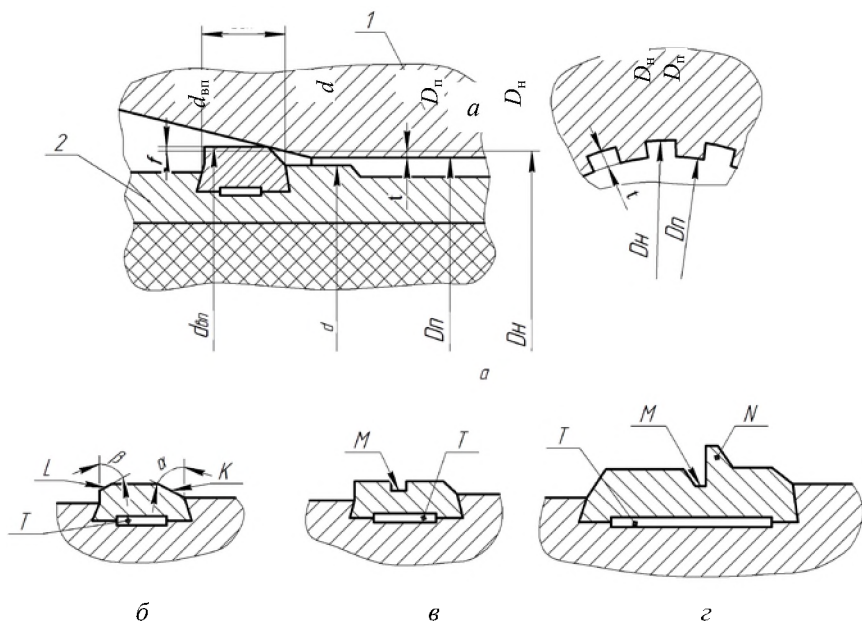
Положение ведущего пояска снаряда в канале ствола орудия при зарядании (*а*) и профили ведущих поясков: цилиндрический (*б*); с кольцевой канавкой (*в*); с буртом (*з*); *I* – ствол; *2* – корпус снаряда;  $d_{\text{вп}}$  – диаметр ведущего пояска;  $d$  – диаметр снаряда по центрующему утолщению (калибр);  $b_{\text{вп}}$  – ширина ведущего пояска;  $D_n, D_n$  – диаметр ствола по полям и дну нарезов;  $t$  – глубина нареза;  $f$  – форсирование ведущего пояска;  $K, L$  – передний и задний скаты;  $M$  – кольцевая канавка;  $N$  – бурт;  $T$  – накатка на дне канавки под ведущий поясок;  $\alpha$  – угол переднего ската;  $\beta$  – угол заднего ската
